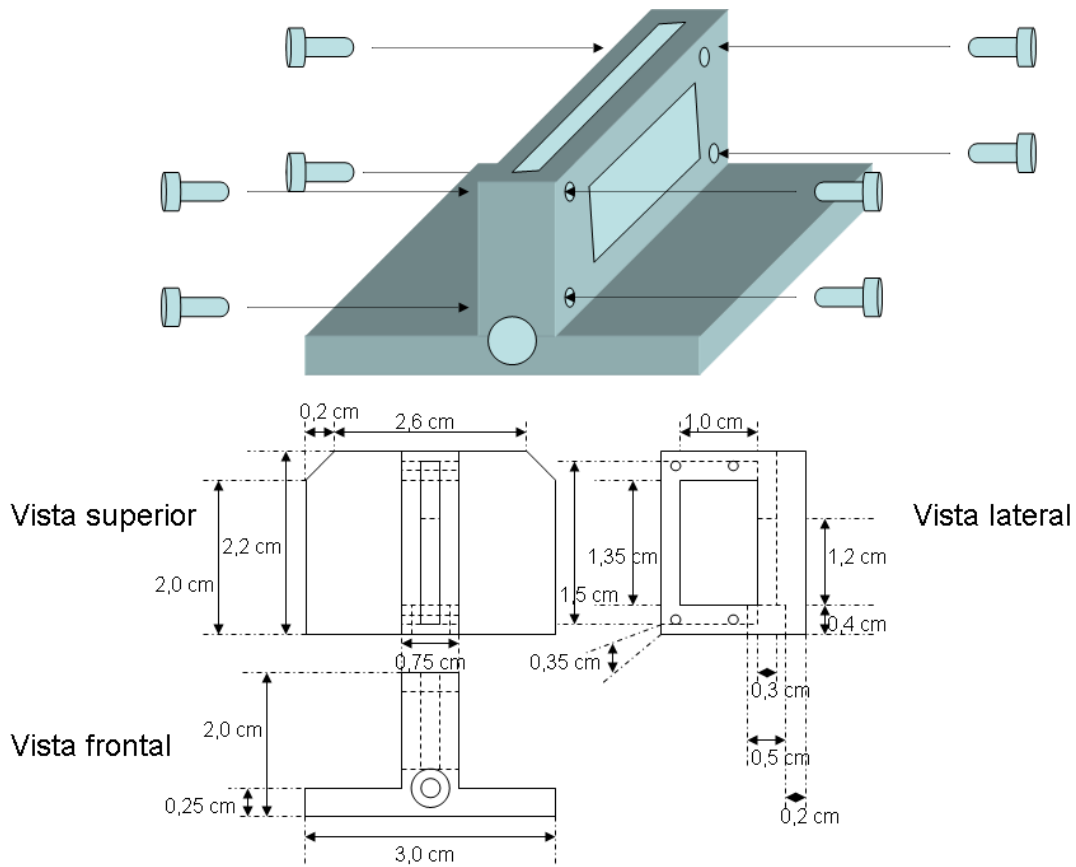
Alzado, planta y perfil del portamuestras de transmisión propuesto.
